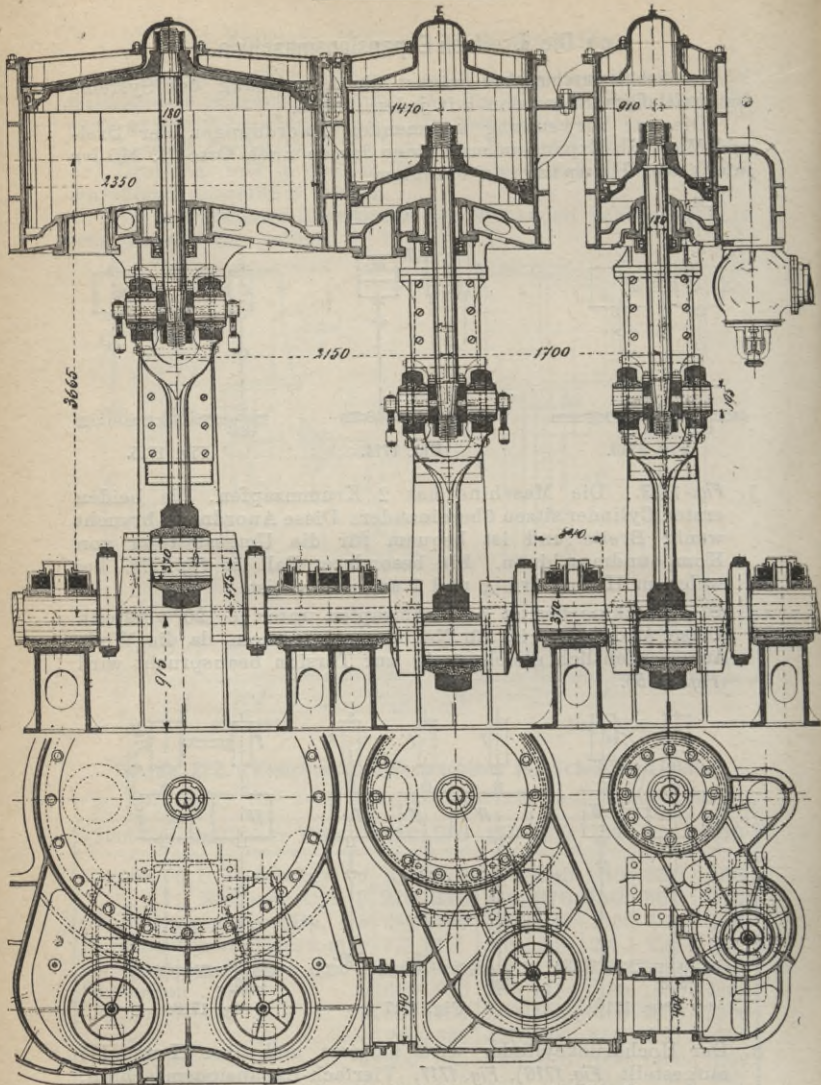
Dreifach-Expansionsmaschine. \*)
